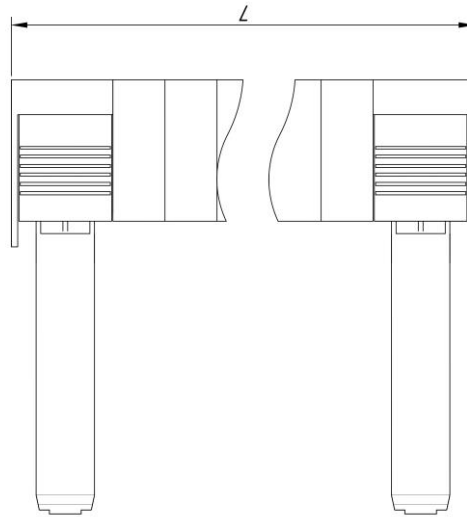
Общий вид холостой крышки ЭПХК. Вид сверху.
